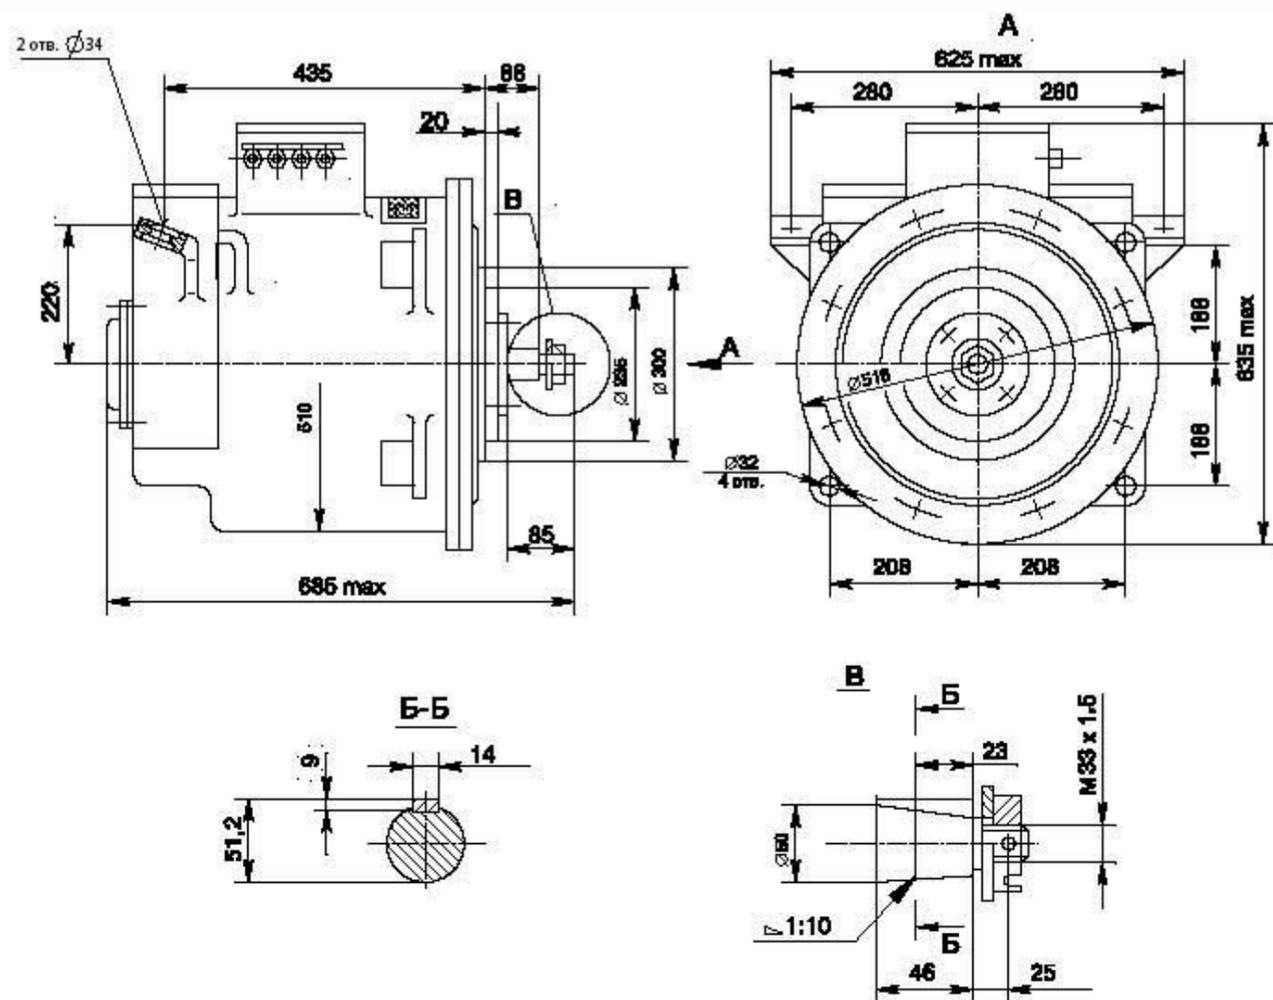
Габаритные и установочные размеры электродвигателя ДТН-33/20Б
